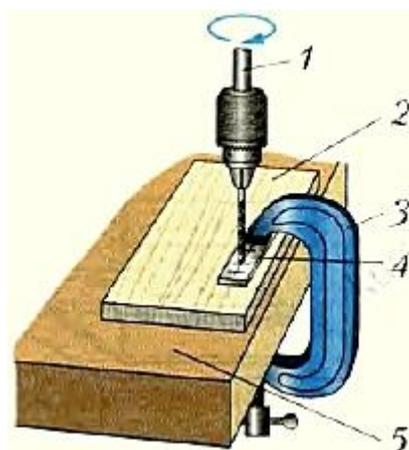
Сверление заготовки, закреплённой на верстаке: 1 — дрель; 2 — подкладная доска; 3 — струбцина; 4 — заготовка; 5 — крышка верстака
